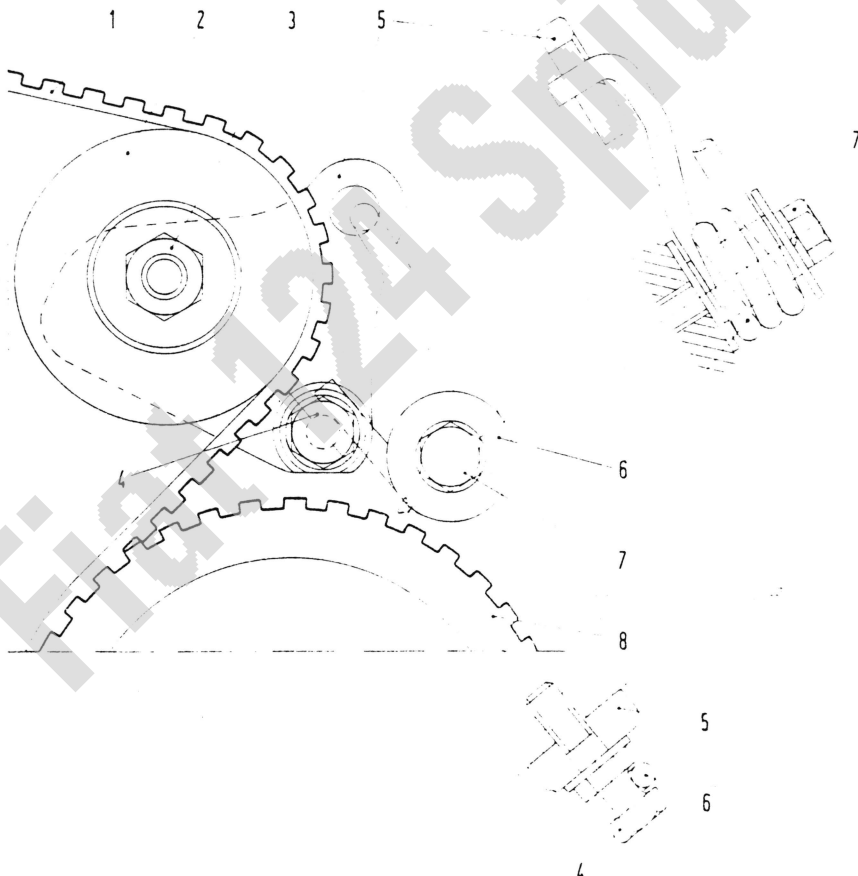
Einbauschema des Riemenspanners mit Feder.
